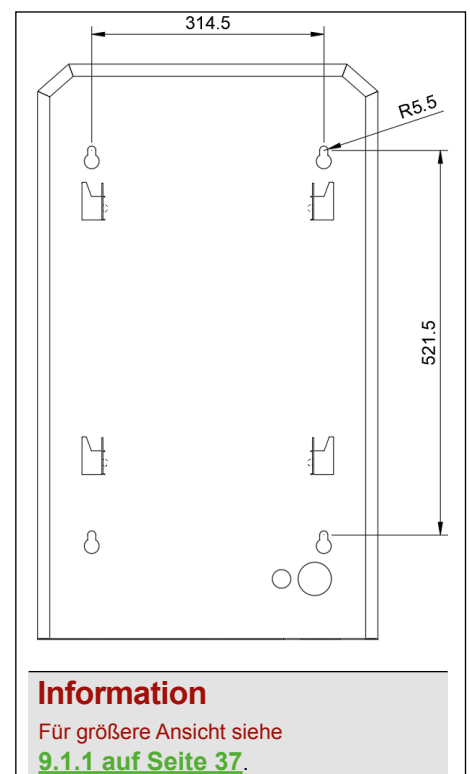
Bohrlöcher Gehäuse Wandhalterung
